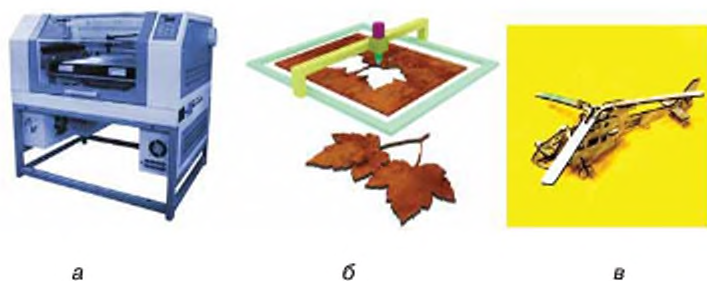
Поздовжньо-фрезерний верстат (а) і формування фрезою фасонної поверхні деревини (б)
